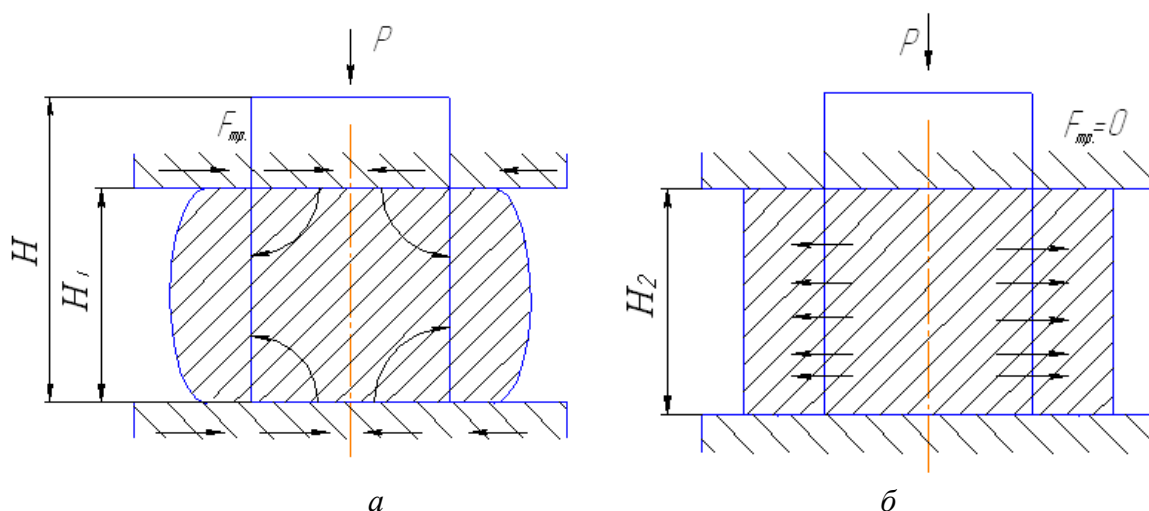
Эскизы поволоков после осадки: a – без смазки; b – со смазкой
